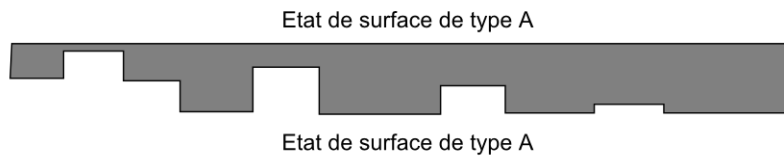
Matériau monolithique avec trous à fond plat - Coupe schématique dans l'épaisseur au niveau d'une rangée de trous de même diamètre
